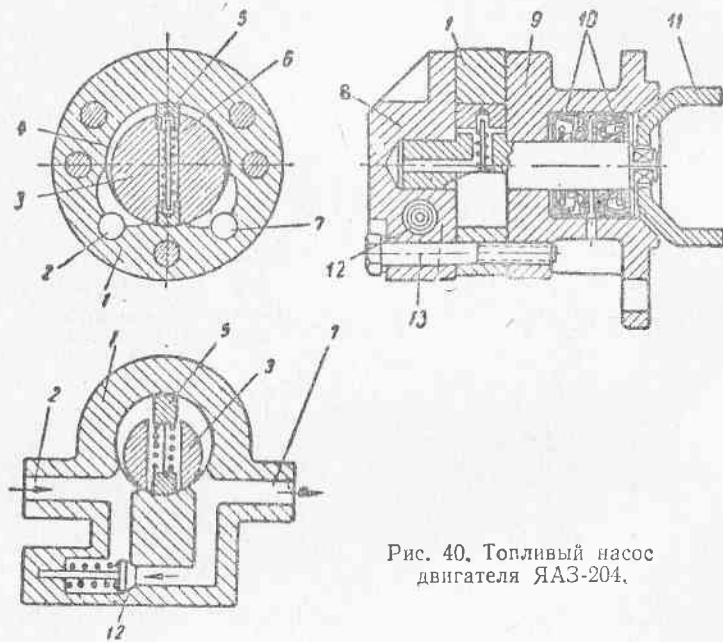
Топливный насос двигателя ЯАЗ-204.
